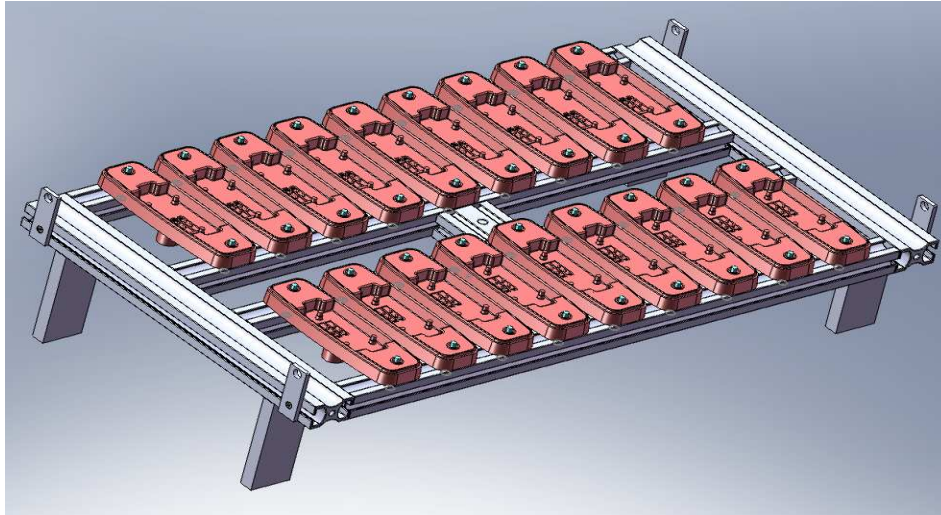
Assembly Suporte 90° F Sidemarker Zeta
